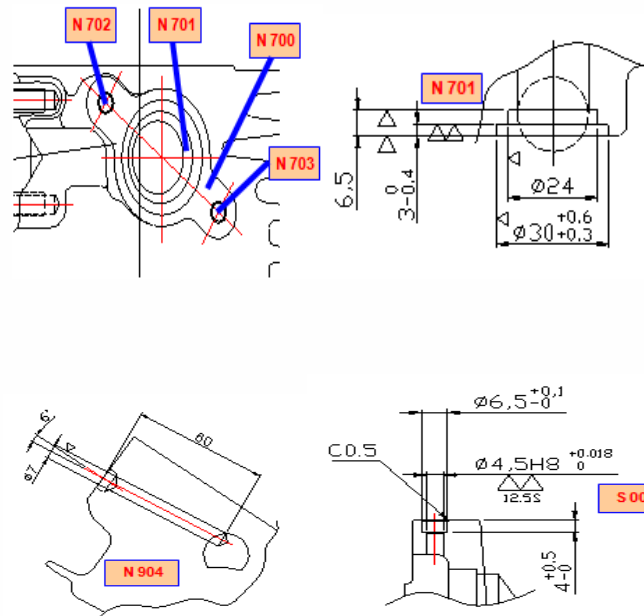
Proses OP 40 *Cylinder Head Machining
